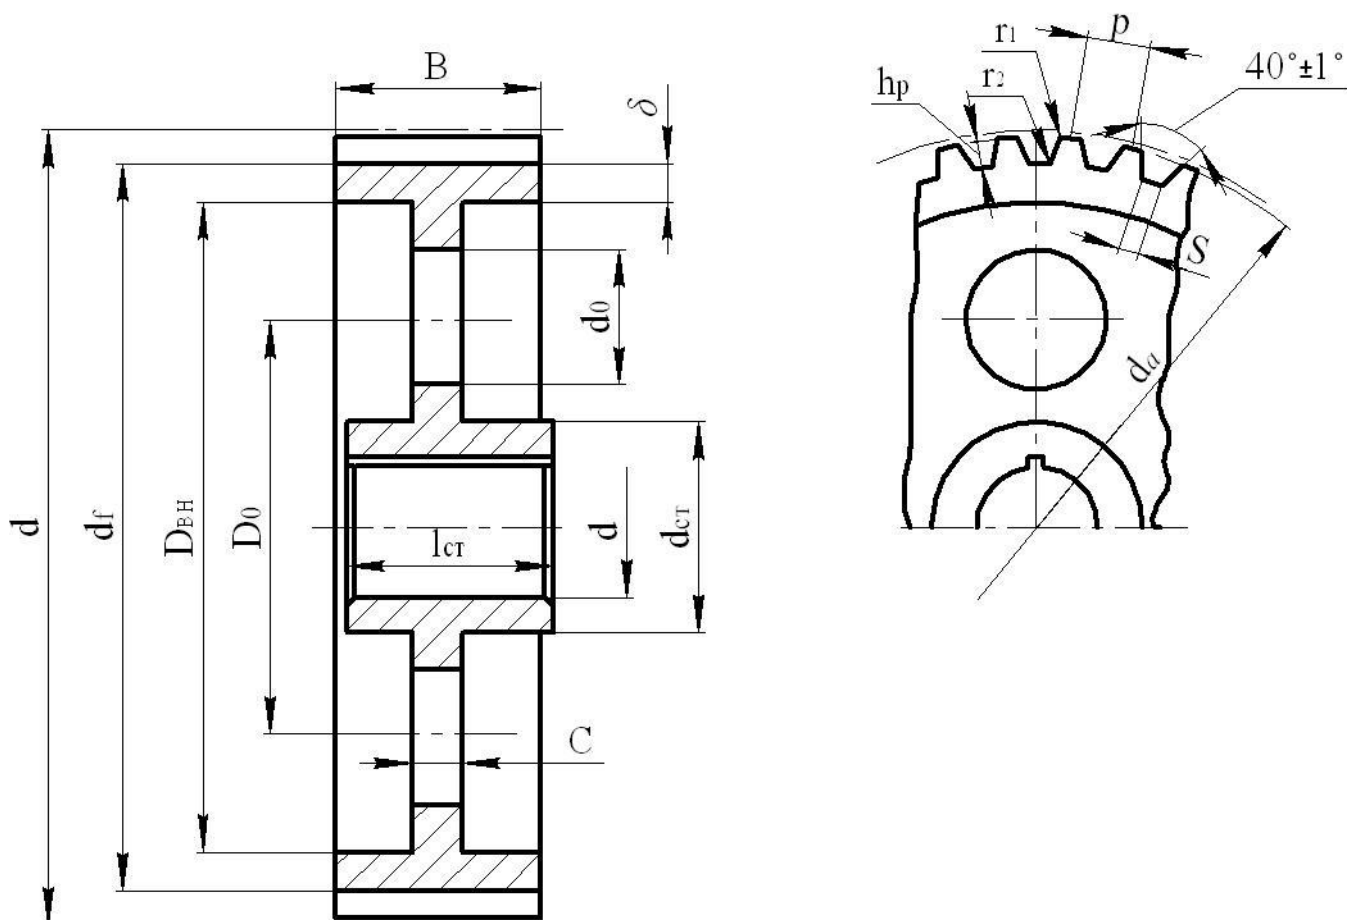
Конструкция шкива передачи зубчатым ремнем
